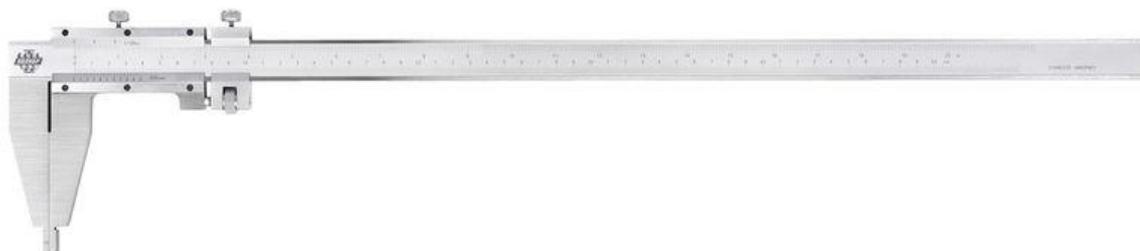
Общий вид штангенциркулей типа ШЦ-III
